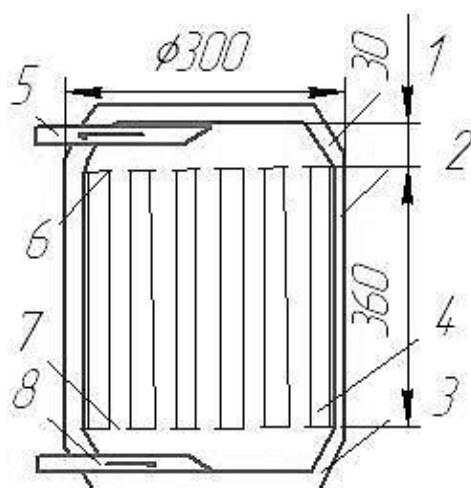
Тепловий акумулятор фазового переходу, адаптований для автобуса ЛАЗ-695Н: 1 – зовнішній корпус; 2 – внутрішній корпус; 3 – теплова ізоляція; 4 – циліндричні капсули; 5 – вихідний патрубок; 6, 7 – пластини з отворами; 8 – вхідний патрубок
